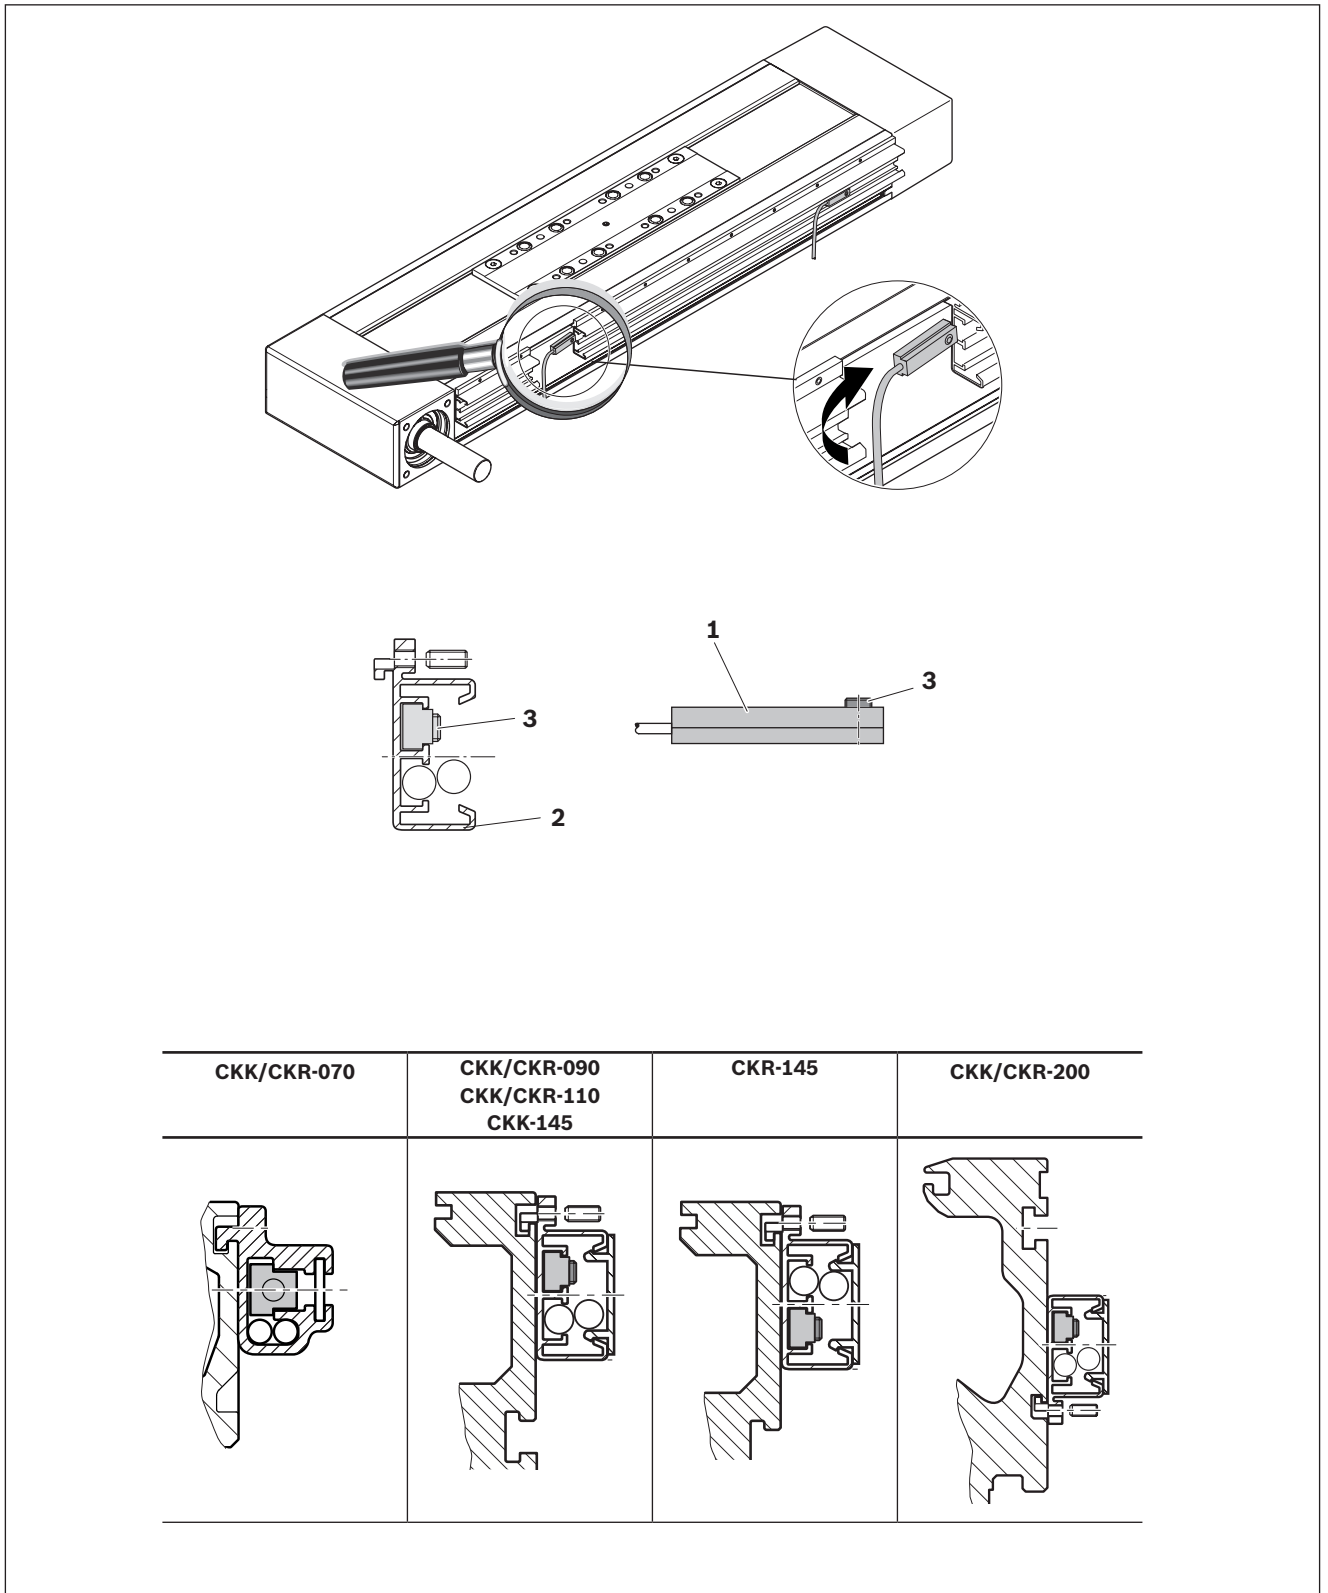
Befestigungskanal/Magnetischer Sensor montieren
